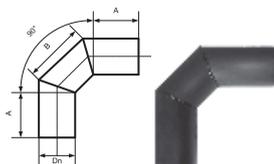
Отвод 90° сварной 3-х сегментный
